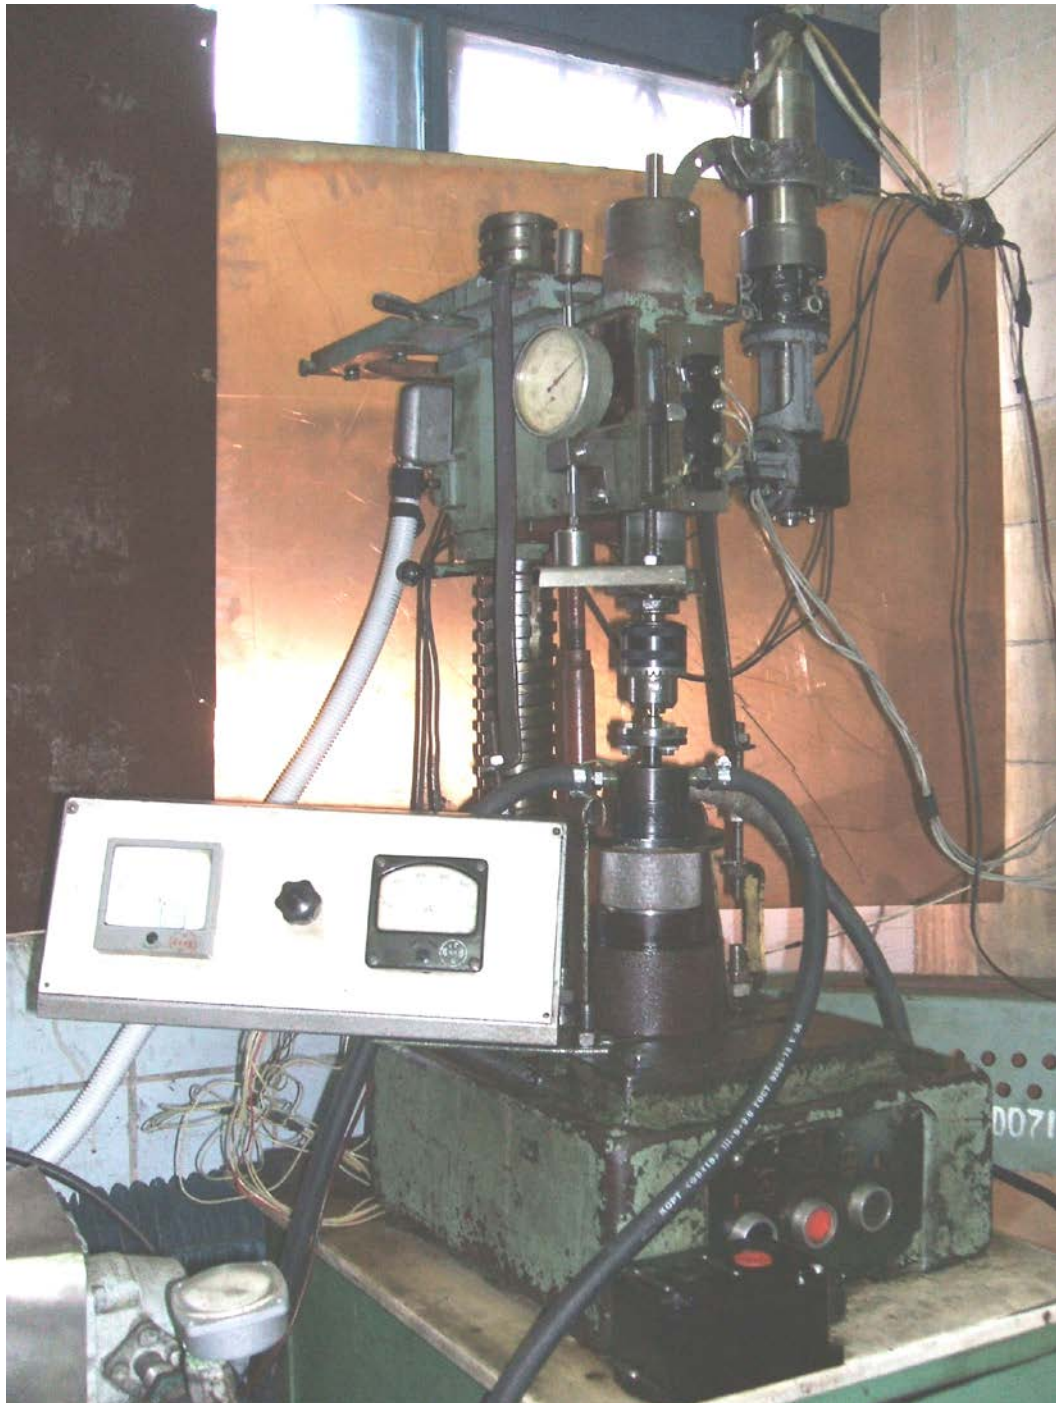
Зовнішній вигляд механічної частини верстату з електроерозійною головкою типу АМН-1.
